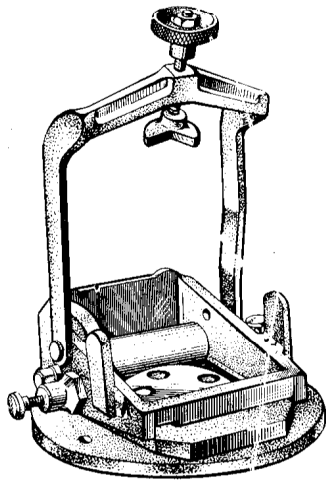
Приспособление для крепления редуктора заднего моста при разборке и сборке
